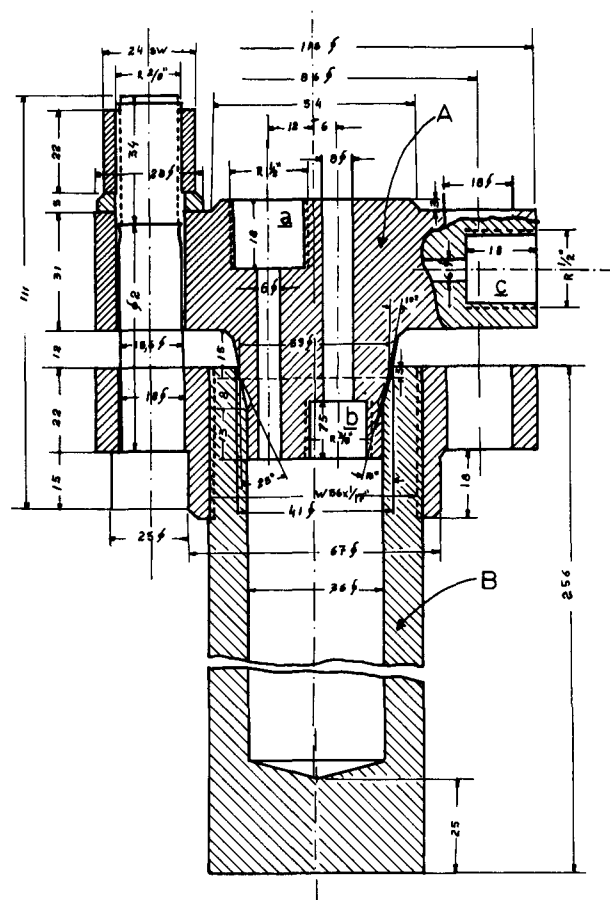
Tampa e recipiente da autoclave de alta pressão. Vista frontal com dimensões.
